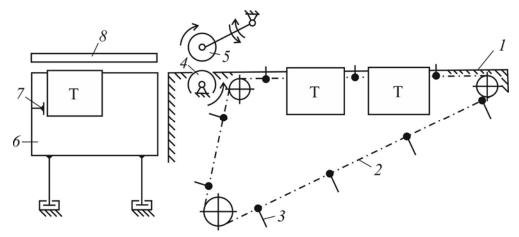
Технологическая линия транспортировки тетрадей: I — седлообразный стол; 2 — цепной транспортер; 3 — упор (поводок); 4 — неподвижный вталкивающий ролик; 5 — подвижный вталкивающий ролик; 6 — качающийся стол; 7 — выравнивающий упор; 8 — обжимная планка; T — тетрадь
